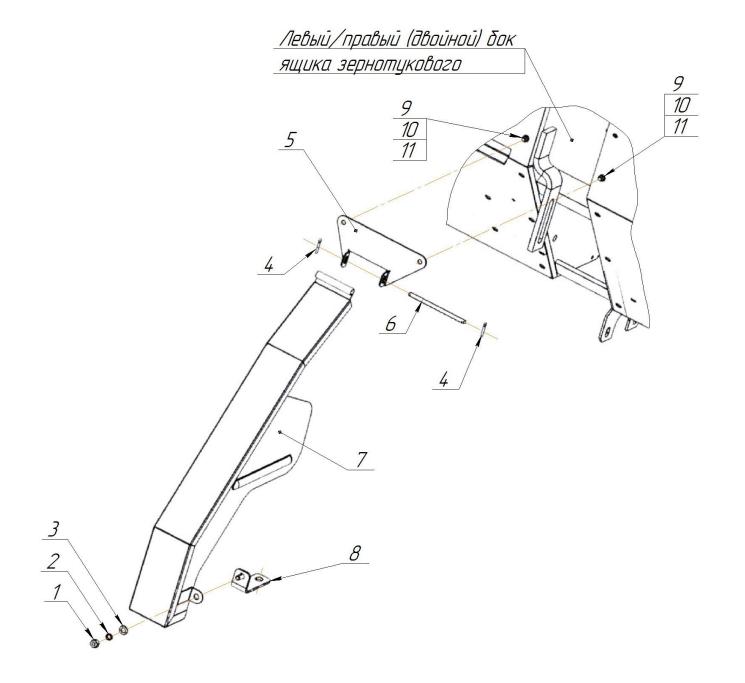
Установка щитков защиты цепей на редуктор и ящик
